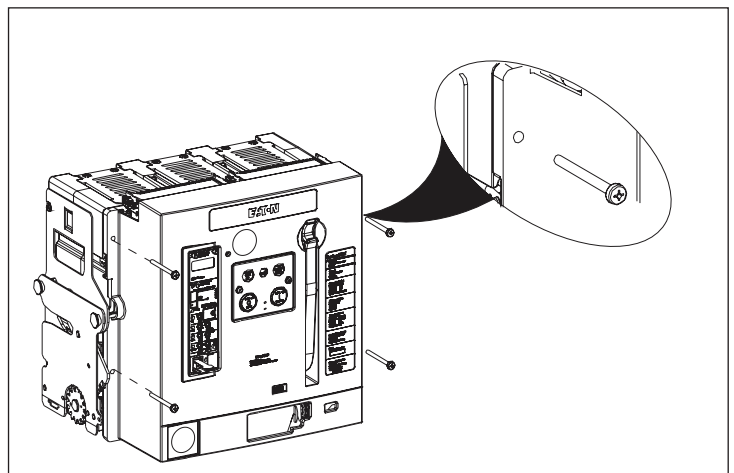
Entfernen der Montageschrauben der Frontabdeckung
